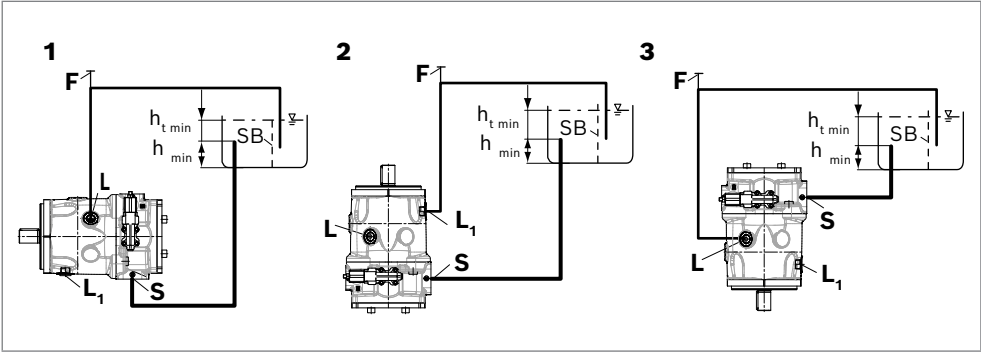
Untertankeinbau A10VZO mit Einbaulage 1–3
